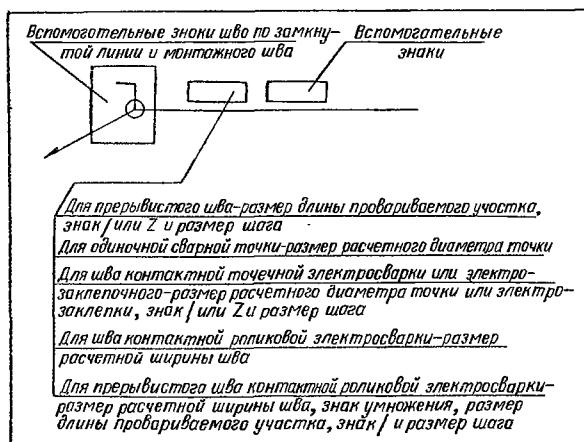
Структура условного обозначения нестандартного шва или одиночной сварной точки
